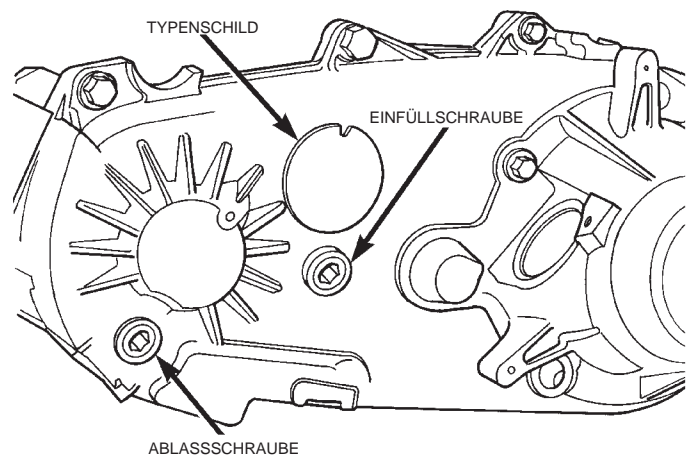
Einfüllschraube, Ablassschraube und Typenschild
